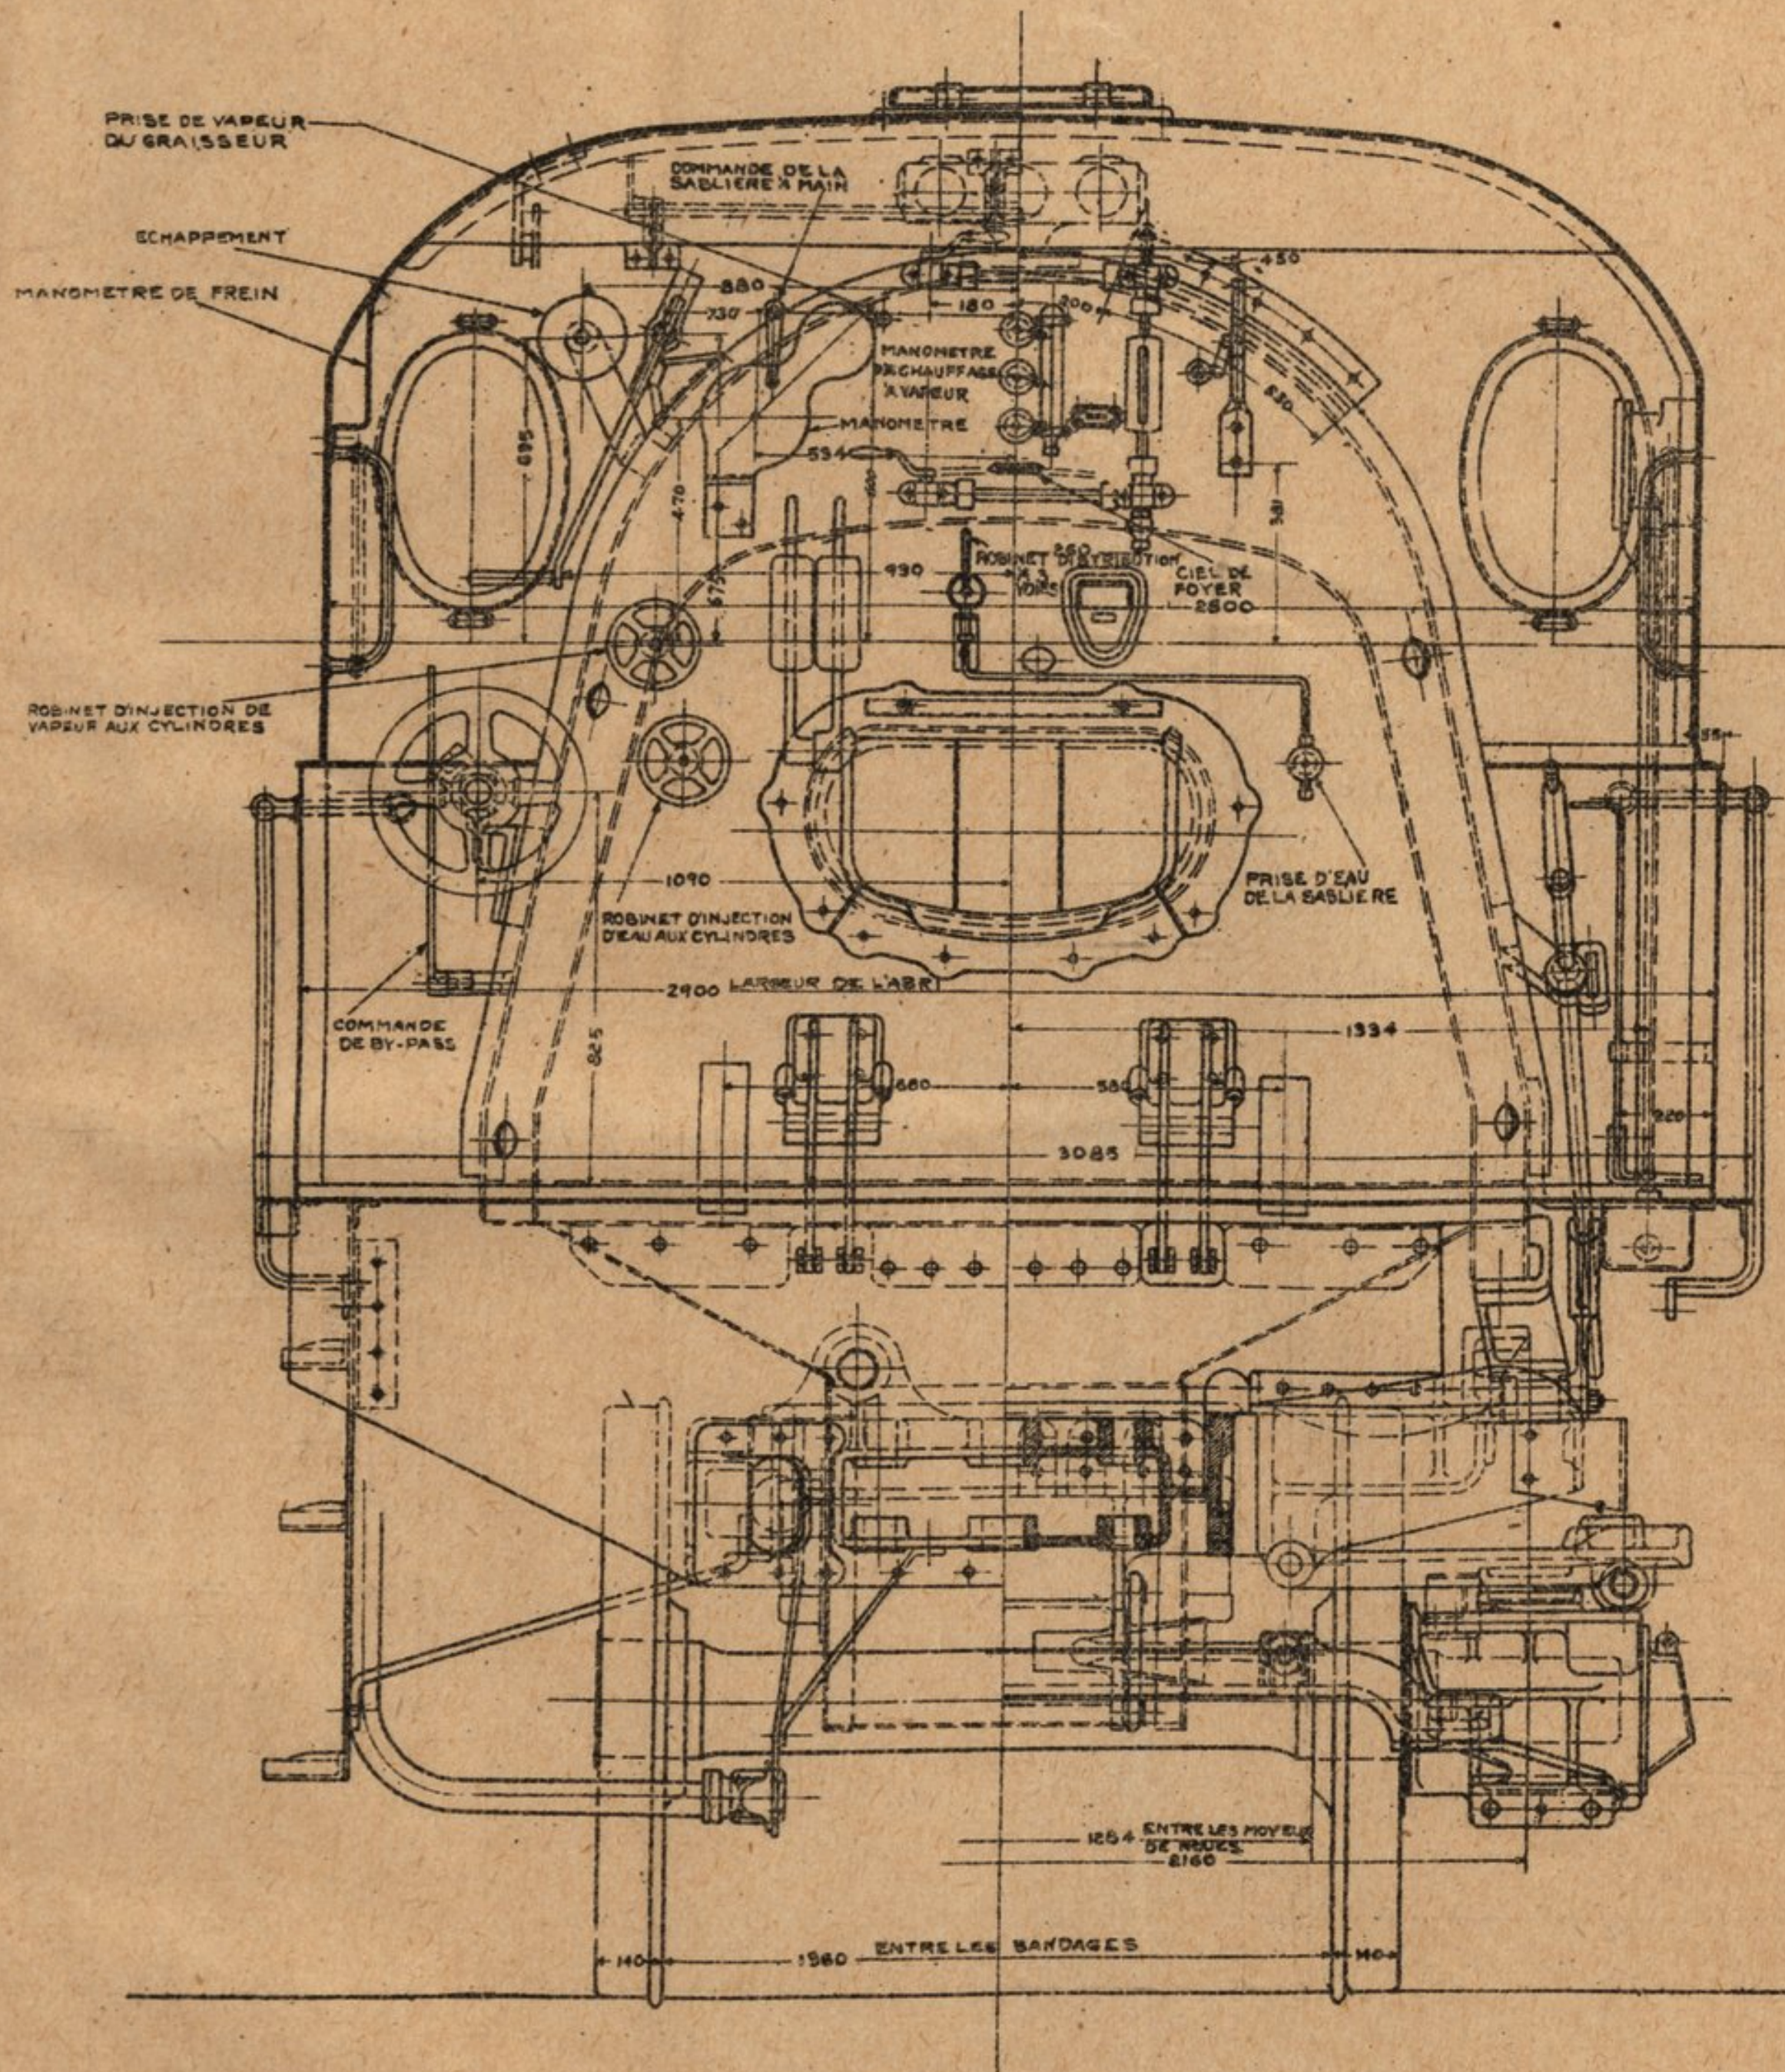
Coupe à l'avant de l'essieu accouplé arrière.
